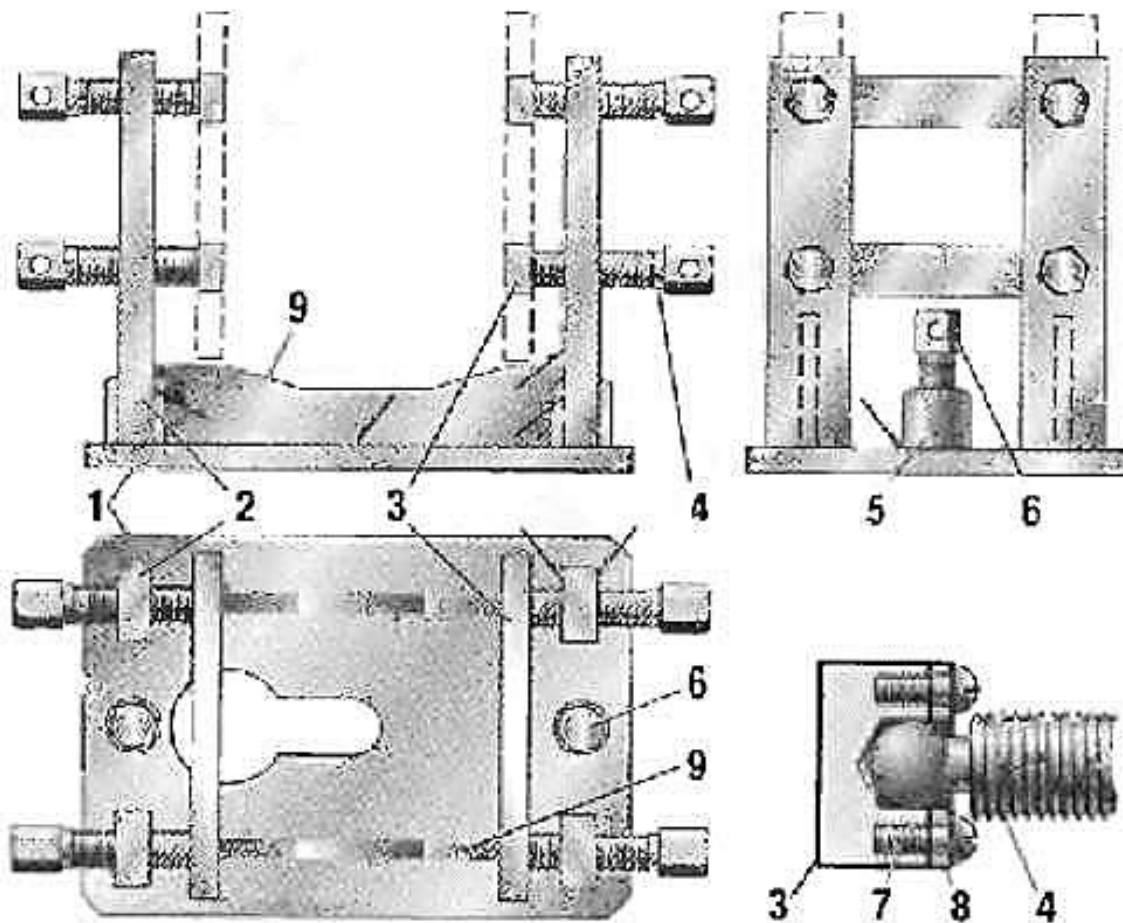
Поворотний стіл: 1 – Опора; 2 – Стійка (4 шт.); 3 – Притискач (4 шт.); 4, 6 – Гвинти (8 шт. і 2 шт.); 5 – Гайка стопорна (2 шт.); 7 – Гвинт М4-8 (16 шт.); 8 – Пластина (8 шт.); 9 – Ребро (2 шт.).
